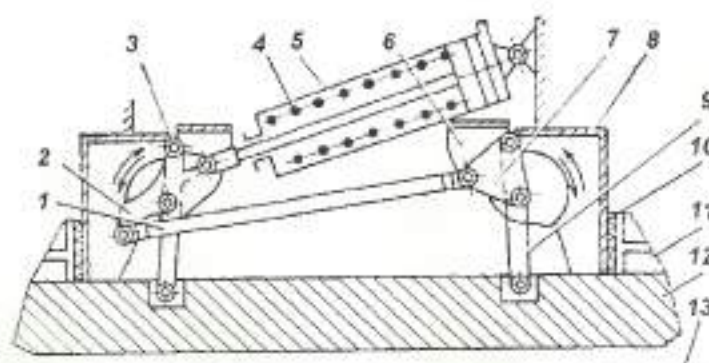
Варіант привода башмака ЕМРГ
